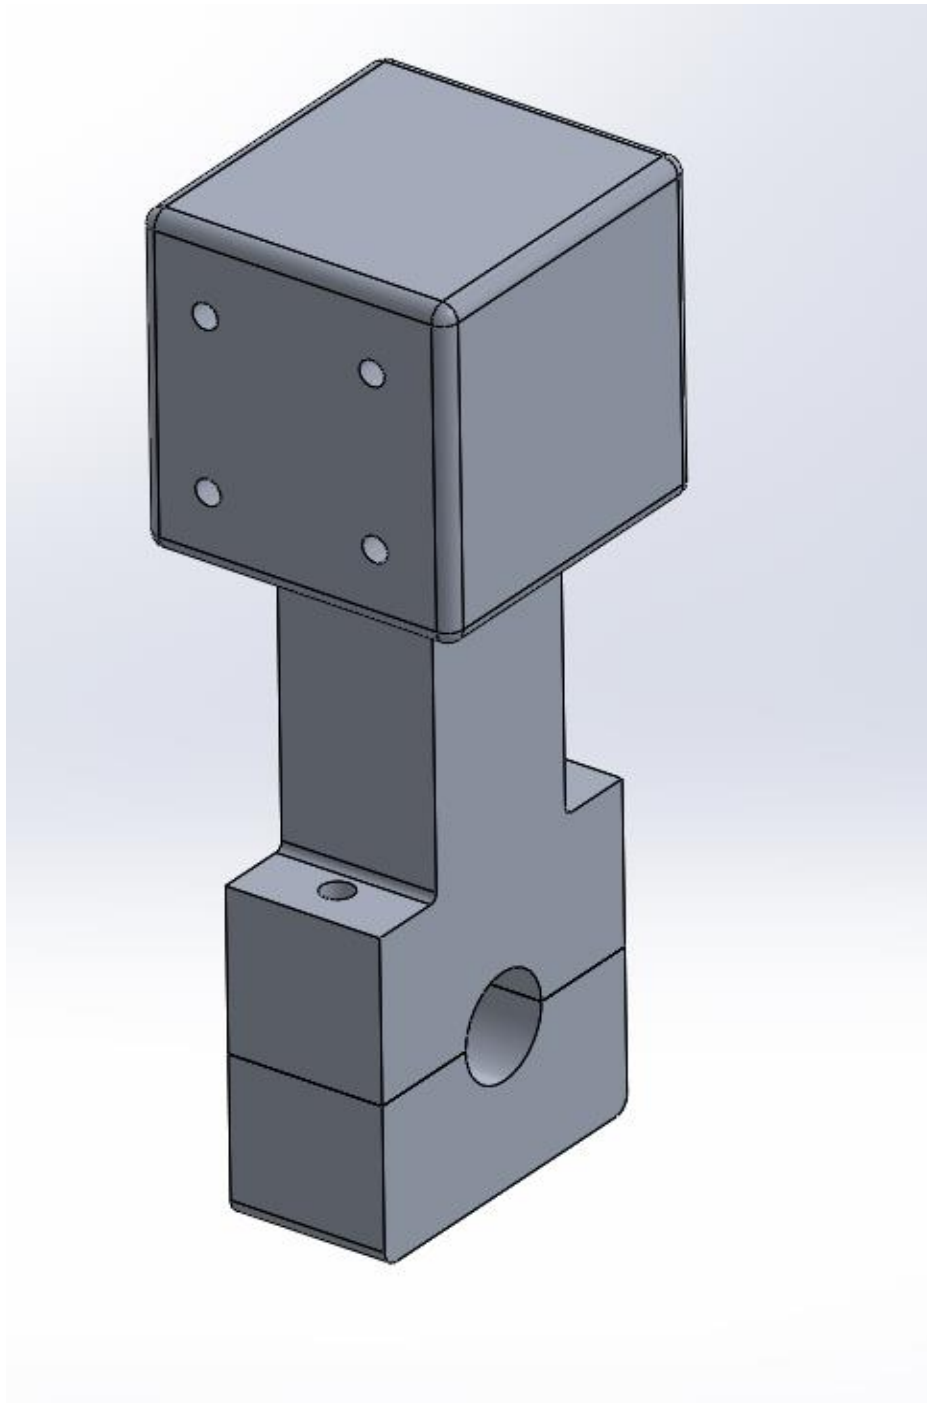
Montaje de la muñequilla que conecta el eje del cabezal y el cilindro neumático
